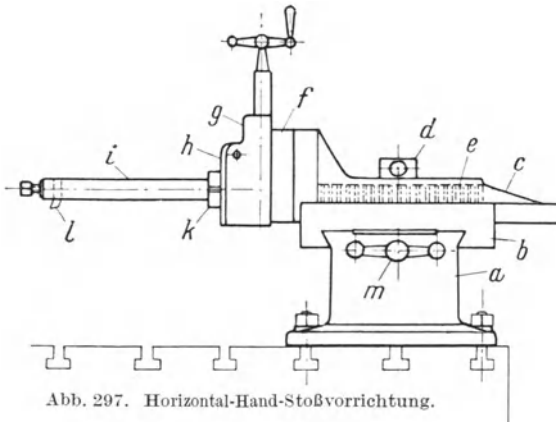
Horizontal-Hand-Stoßvorrichtung.
